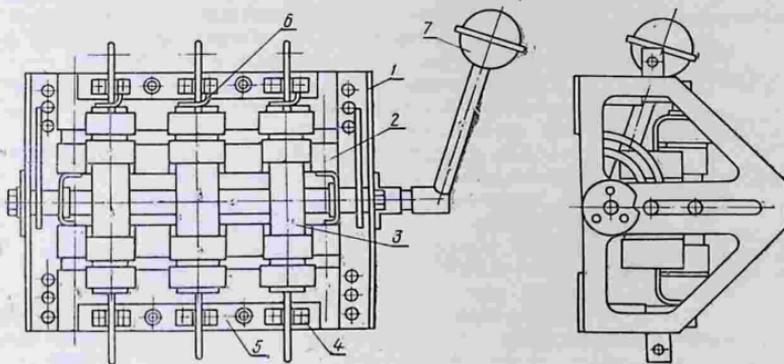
Трехполюсный блок рубильник—предохранитель серии РП с боковой рукояткой:
